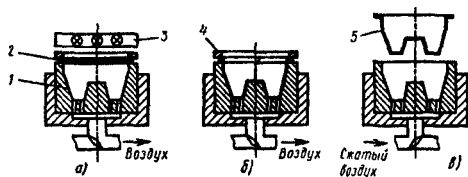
Схема установки для вакуумного формования: а — разогрев листа, б — отсос воздуха, в — выталкивание изделия сжатым воздухом; 1 — матрица, 2 — заготовка, 3 — плита разогрева, 4 — прижимная плита, 5 — готовое изделие
